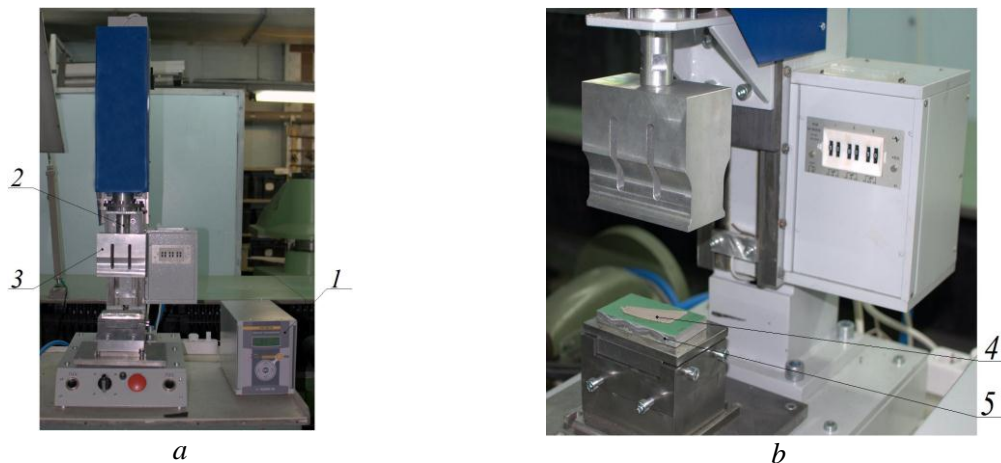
Установка для ультразвуковой опрессовки края обувной резинки:
